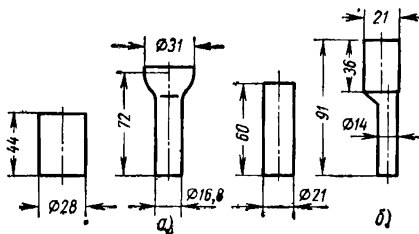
Однопереходная штамповка поковок: а — шарового пальца; б — шпильки опоры поперечины
